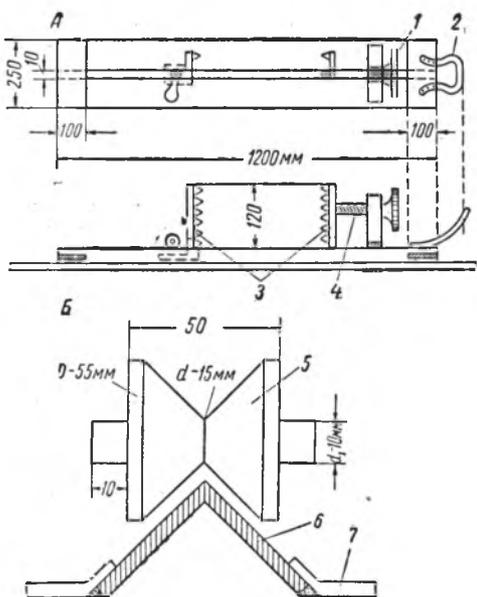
Подвижная каретка: А — вид сверху; Б — вид сбоку. 1 — маховичок; 2 — ручка; 3 — зажимное приспособление; 4 — трехзаходный червяк; 5 — ролик каретки; 6 — полозок каретки (из уголкового железа); 7 — крепление полозков (приварить или заклепать).
